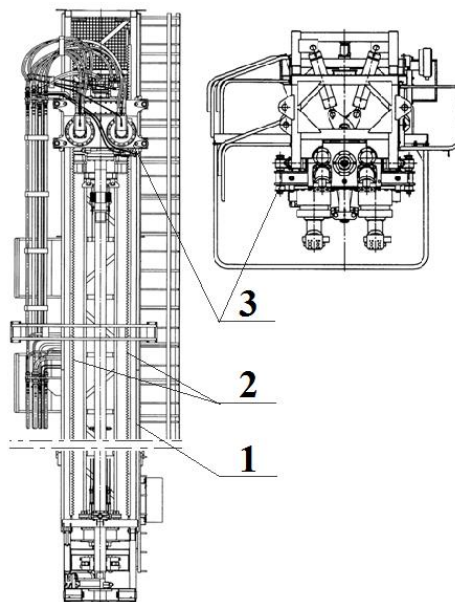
Мачта станка СБШ–160/200–40: 1 – мачта, 2 – зубчатая рейка, 3 – каретка.
